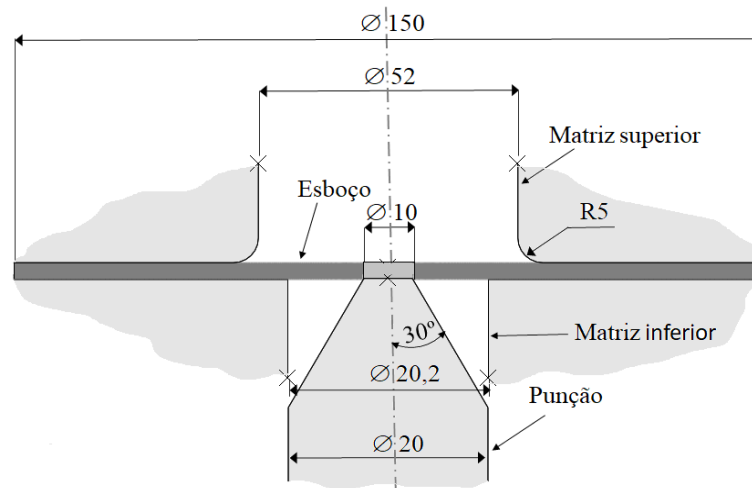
Esquema do ferramental do ensaio de expansão de furo com dimensões em [mm].
